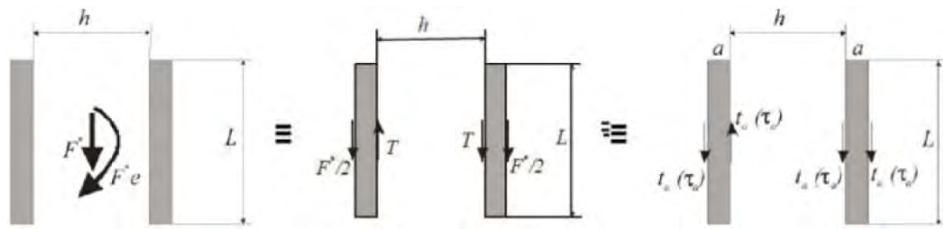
26 Cordón de soldadura en la plancha metálica
